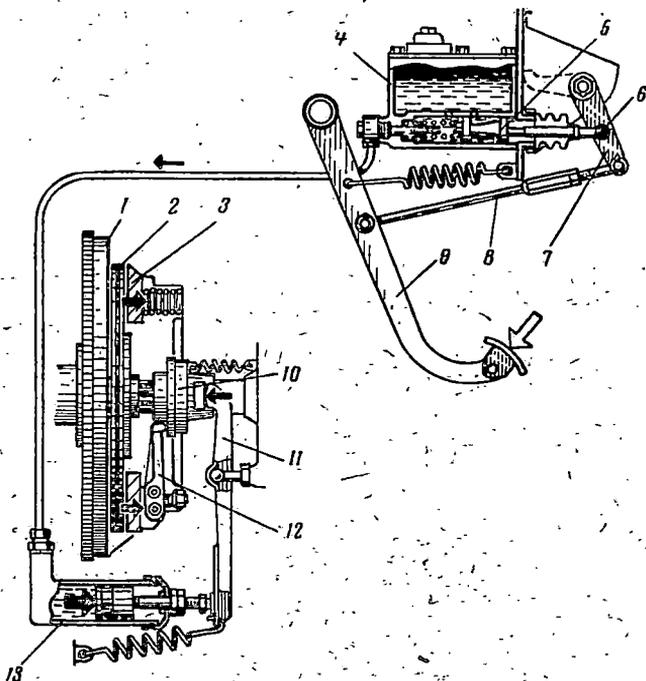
Схема гидравлического привода сцепления автомобиля ГАЗ-66:
